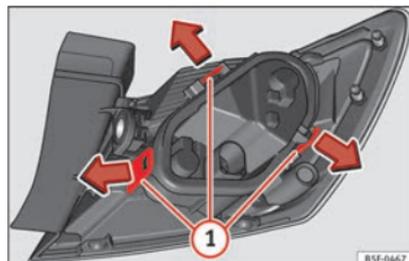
Linguetta di fissaggio nella parte posteriore del fanale di coda.
